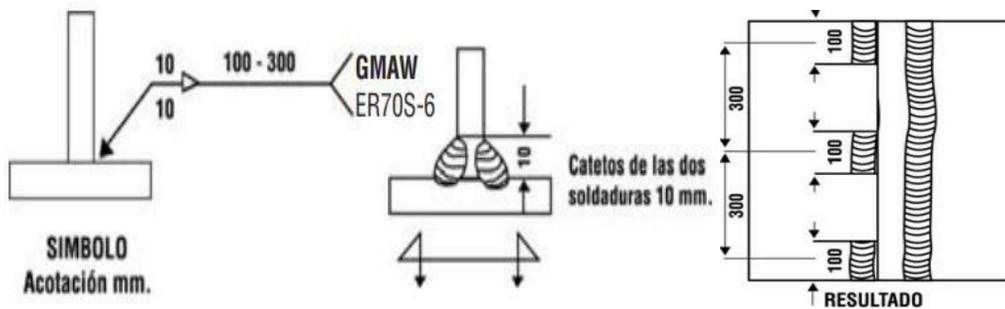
Ejemplo para soldadura doble en ángulo interior
